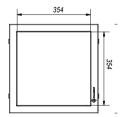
Maßzeichnung des Heizgerätes TORCH Puc.1.
